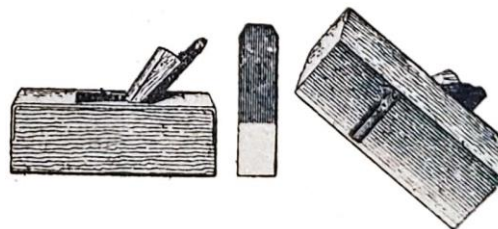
Rebote. Ilustração de COLARES, 19--: 20.
